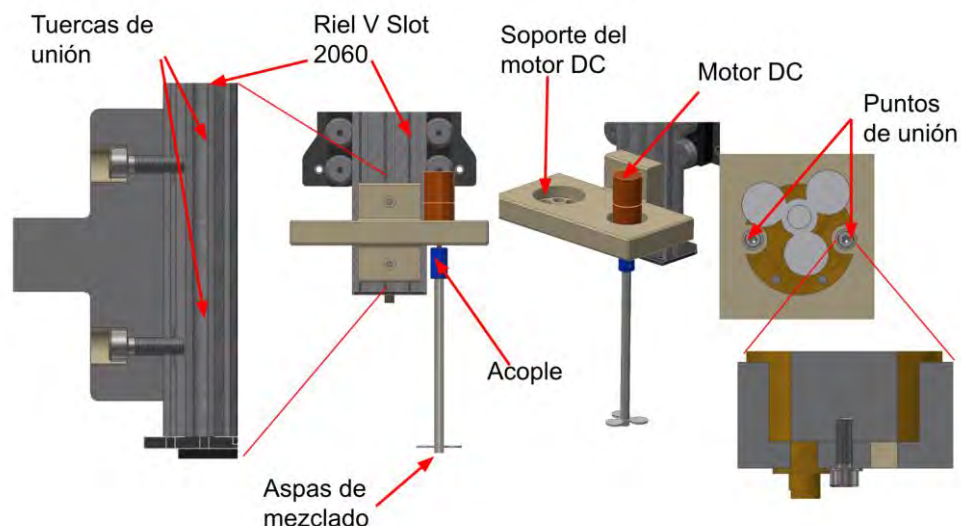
Conjunto de Motor DC y aspas de mezclado con soporte
